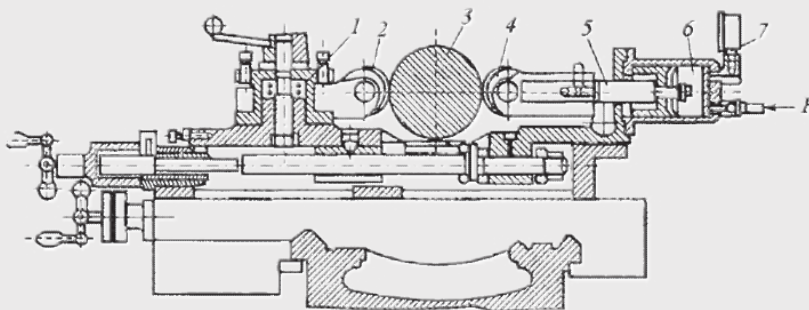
Гідравлічний двороликовий обкатний пристрій: 1 — супорт токарного верстата; 2, 4 — ролики; 3 — деталь; 5 — шток; 6 — гідроциліндр; 7 — манометр
